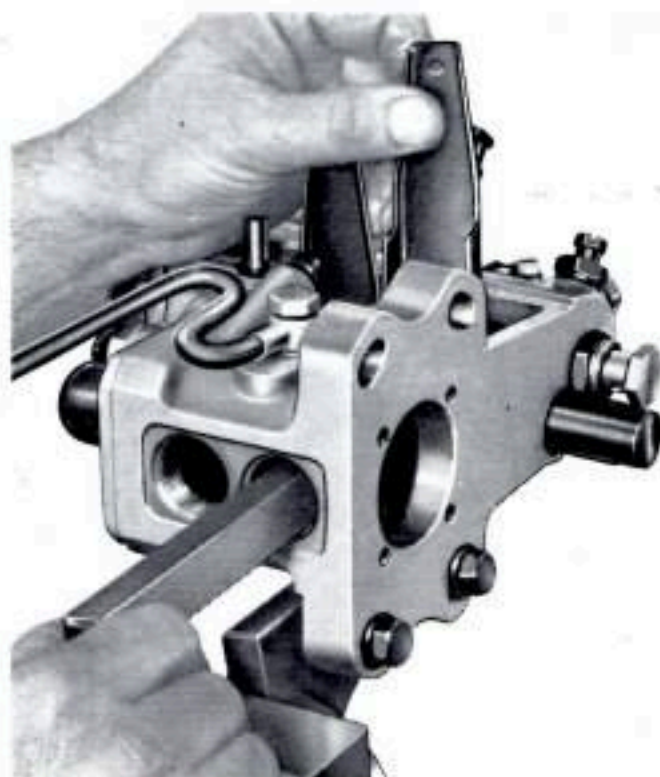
Estrazione delle punterie dalle rispettive sedi.
